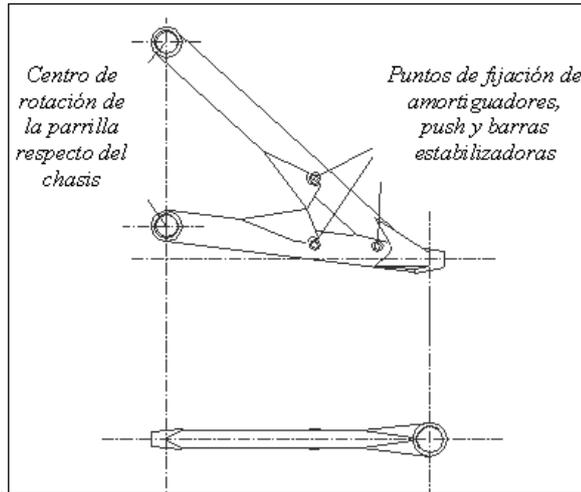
Parrilla inferior – Puntos de anclaje y fijación
